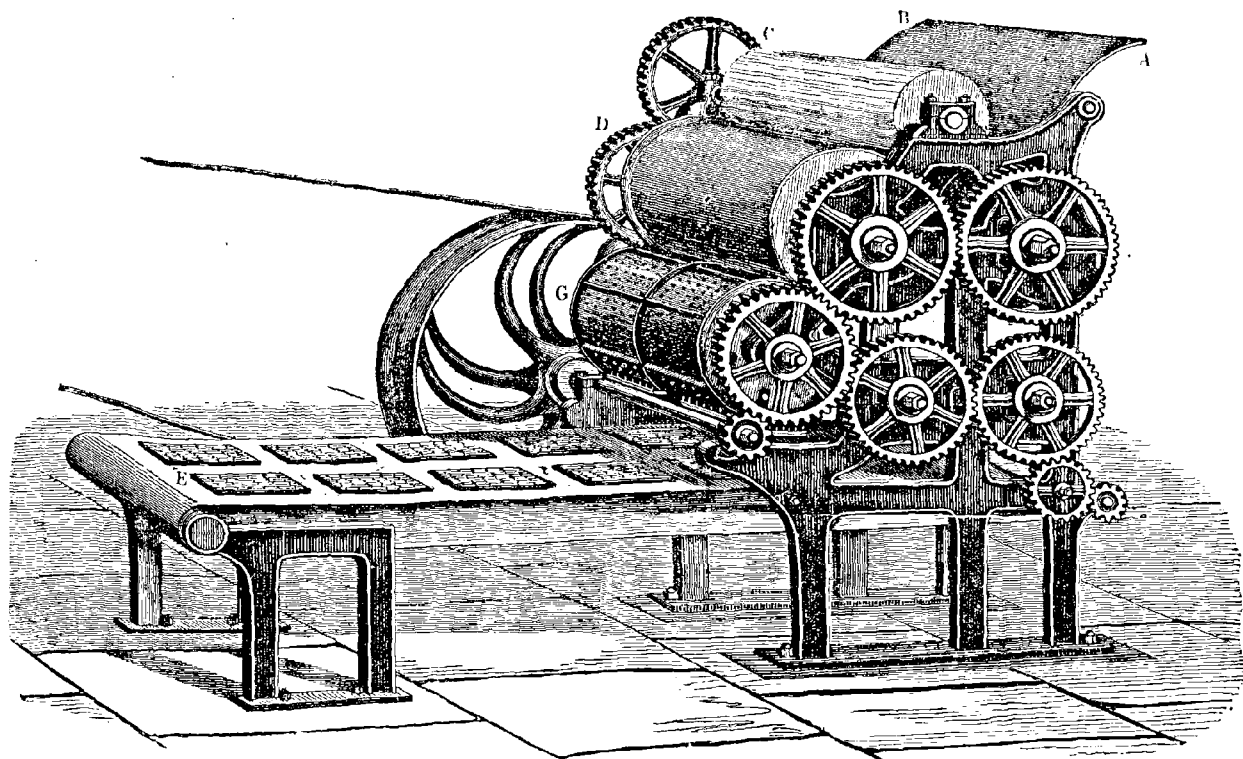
Machine pour découper et rouler les biscuits de mer.
